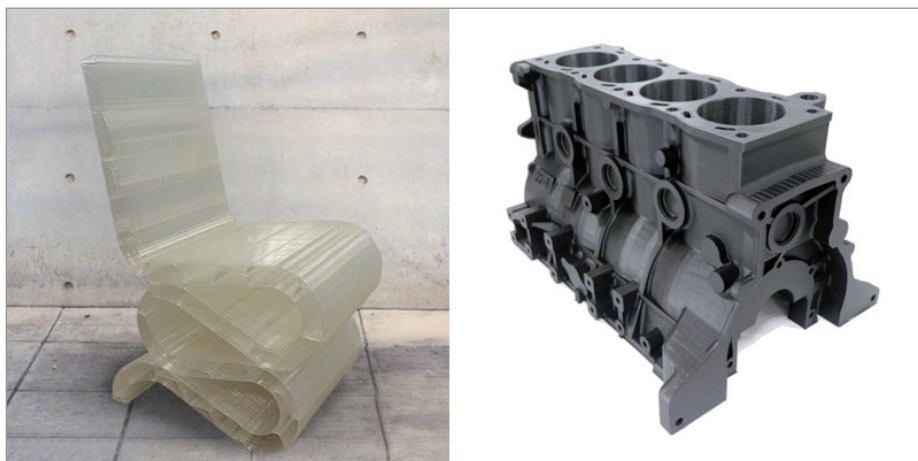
Изделия, созданные с помощью Super Discovery 3D Printer: кресло (материал: 3D850, размеры: 45x50x95 см, вес: 18 кг), прототип двигателя внутреннего сгорания (материал: Premium PLA, размеры: 100x60x50 см, вес: 5,5 кг)
